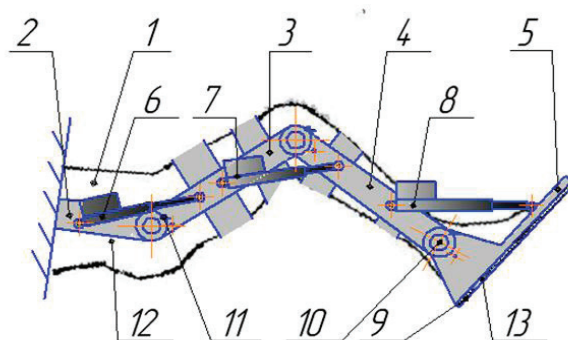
Схема конструкции ноги экзоскелета человека (вид сбоку): 1 — Нога человека; 2 — Стойка; 3 — Бедренное звено; 4 — Голень; 5 — Стопа; 6, 7, 8 — Приводы линейного перемещения; 9 — Резиновая подошва; 10 — Датчик угла поворота (энкодер); 11 — Предохранительный концевой датчик; 12 — Ремни для укрепления на ноге человека; 13 — Датчик нагрузки на опорную пяту. [4]
